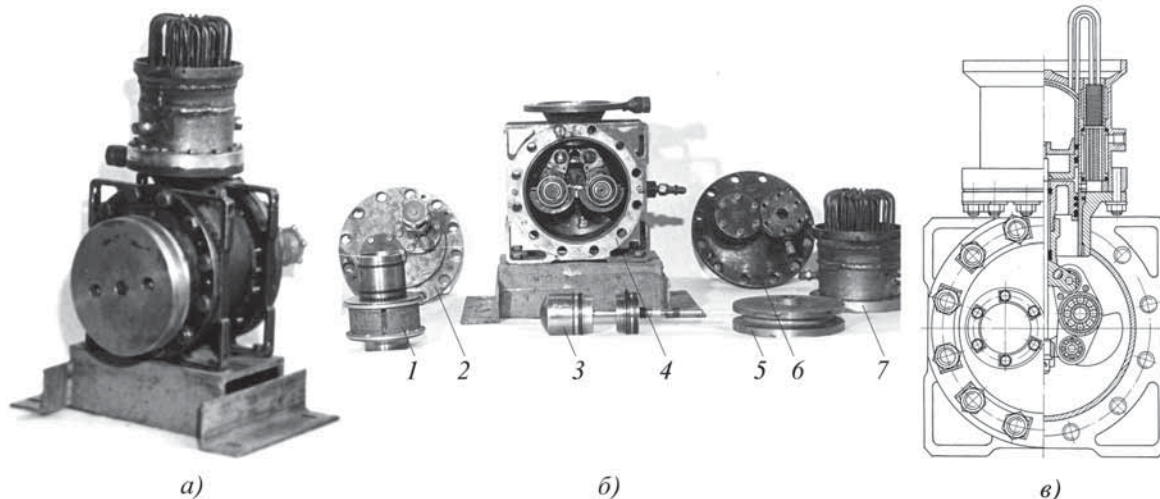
Внешний вид (а) двигателя ДС 6,5/3,0 Т, его узлы и детали (б) и его устройство (в):
